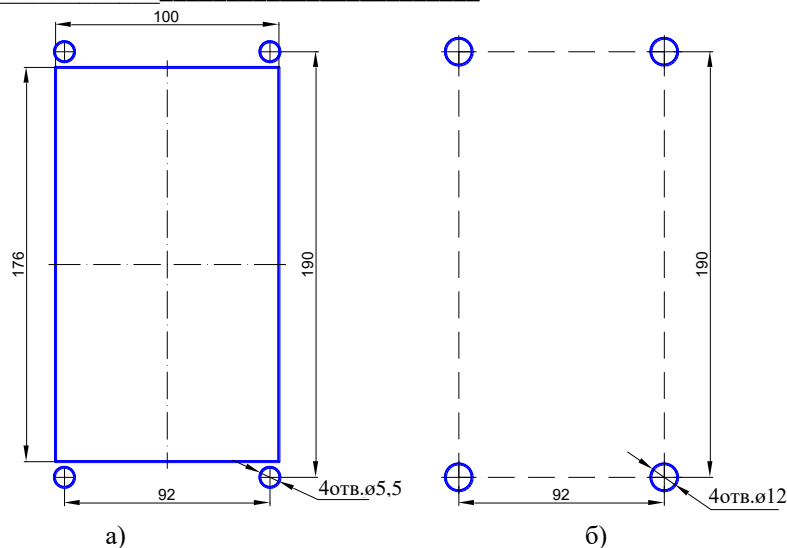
Разметка под крепление DPU5000-KEDC-IP а) снаружи; б) изнутри
